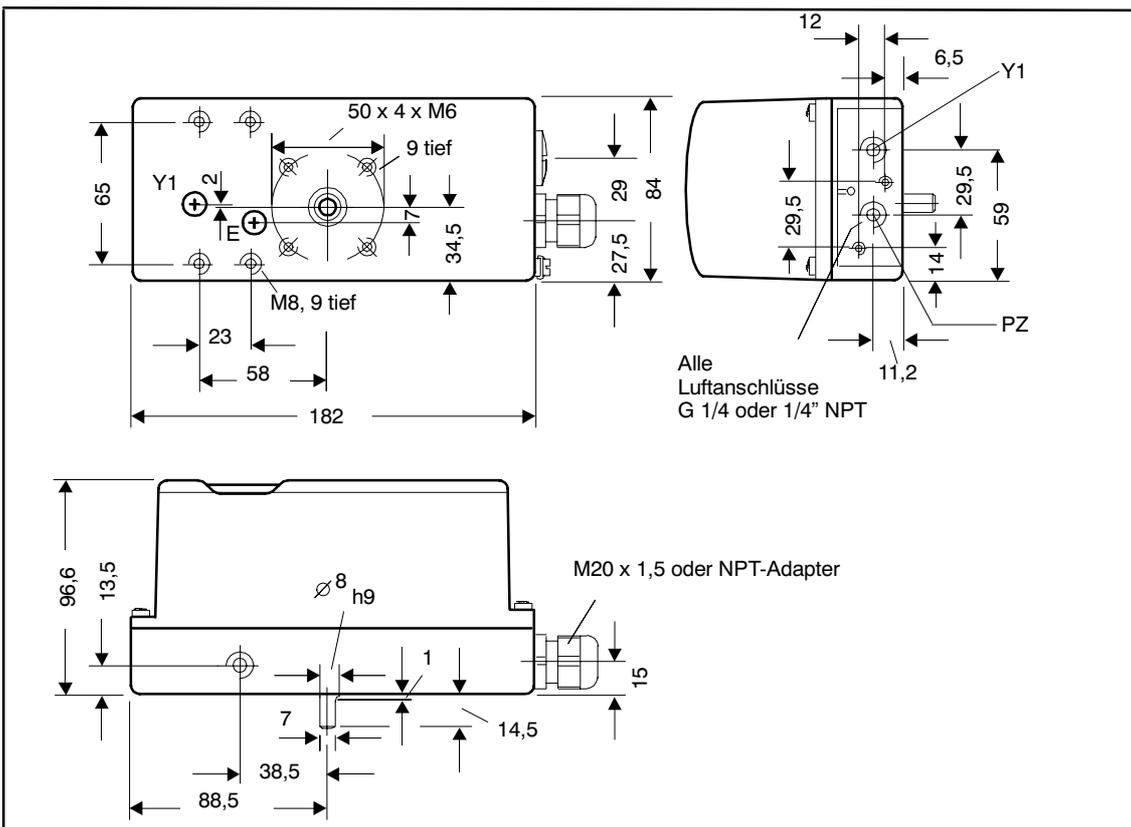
Maßbild Ausführung Metallgehäuse 6DR5xx1
